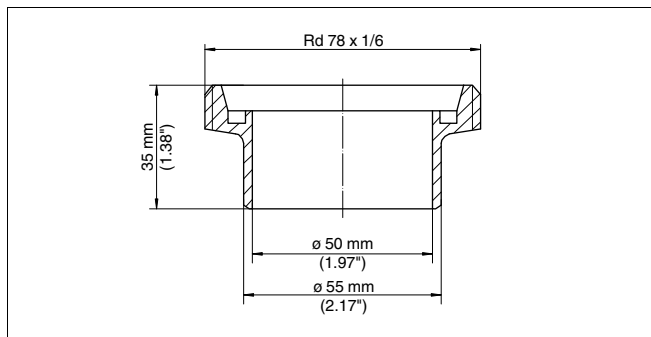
Размеры приварного штуцера - накидная гайка DN 50 по DIN 11851
